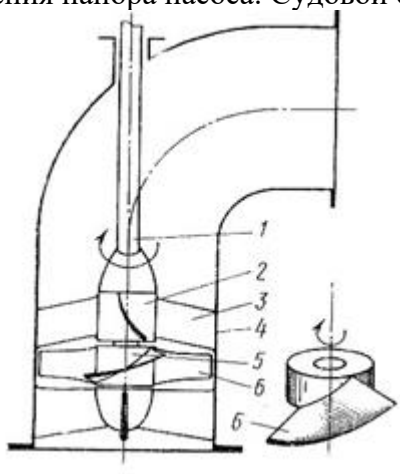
Схема осевого насоса: 1 - вал; 2,5 - обтекатели; 3 - направляющие лопасти; 4 - корпус; 6 - лопасти пропеллера.
